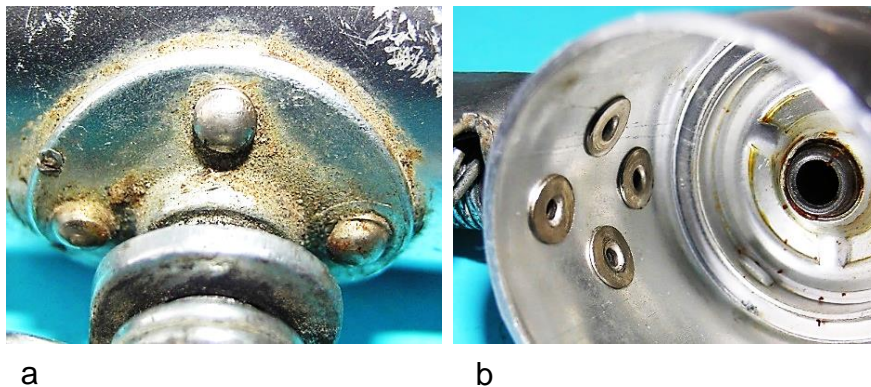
Befestigung des Flansches am Gehäusemantel mit Hohlrieten:
